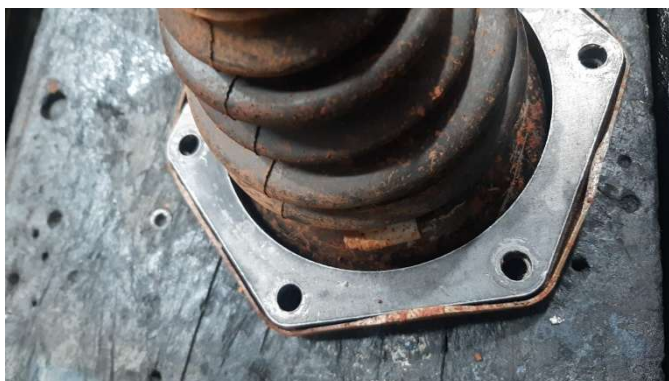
chapa de reforço da flange da capa do semieixo.
